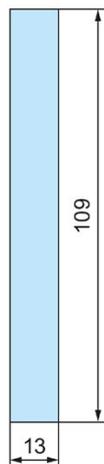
Croquis acotado de las tiras rotulables para módulos de 25 mm
